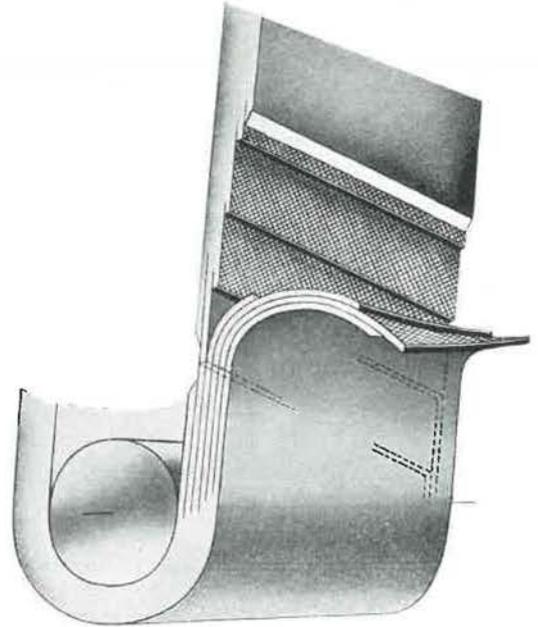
Découpe des extrémités de deux courroies qui doivent être soudées l'une à l'autre.
